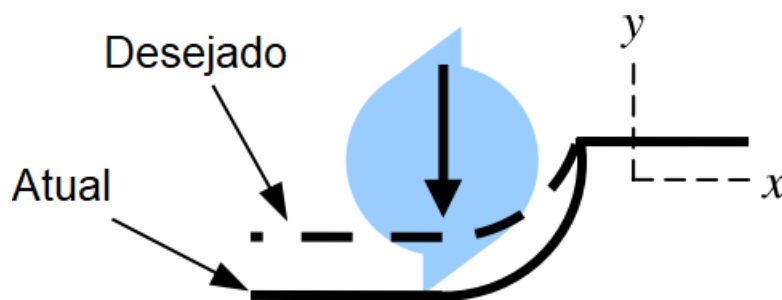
Superfície com corte excessivo no fresamento concordante devido à posição da aresta da ferramenta na saída do corte. O erro é denominado como vibrações da direção  $y$  [58]
